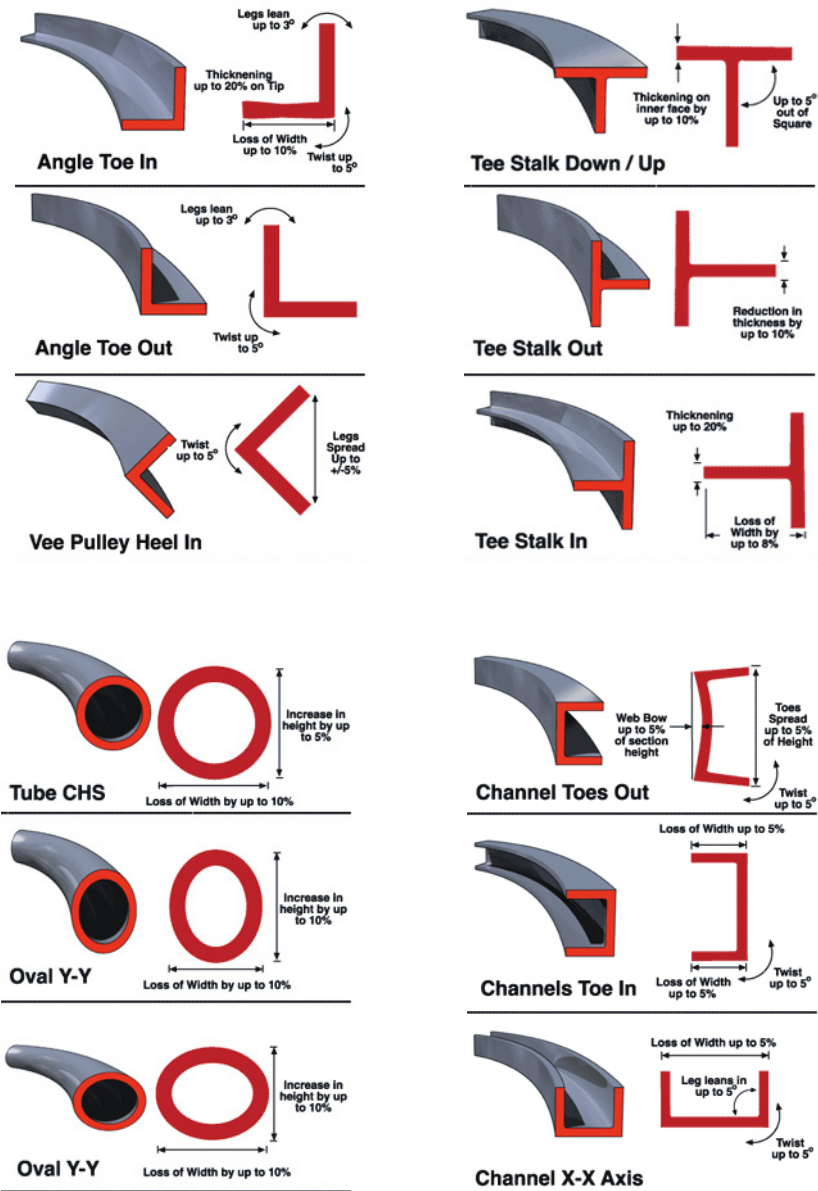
Toepassingsvoorbeelden voor buigwalsen
